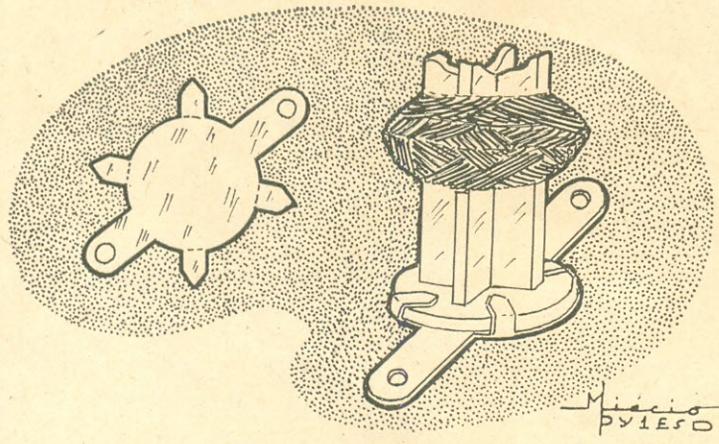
Detalhe mostrando como deve ser confeccionado o suporte para fixação do reator ao chassi.
